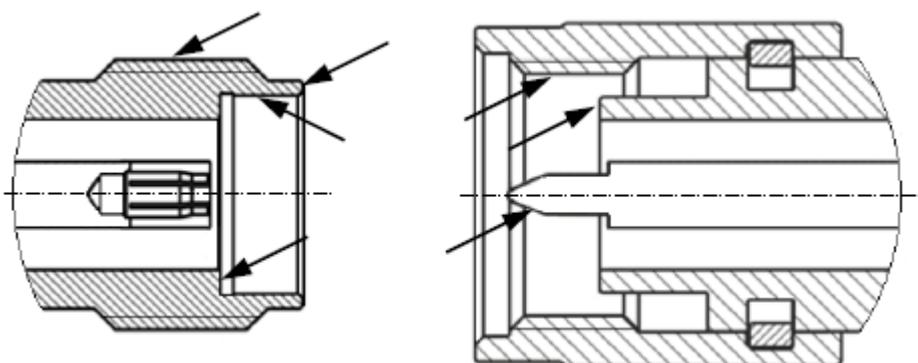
Соединители тип 3,5 мм (розетка слева, вилка справа)
